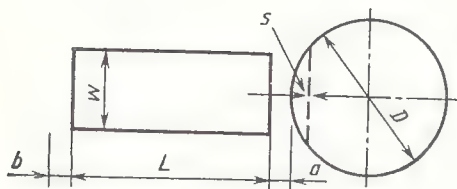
Расположение фрезы и детали (оси детали и фрезы находятся на одной прямой):
